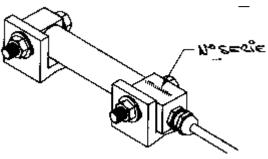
Soldadura del soporte de montaje del transductor y la barra espaciadora
